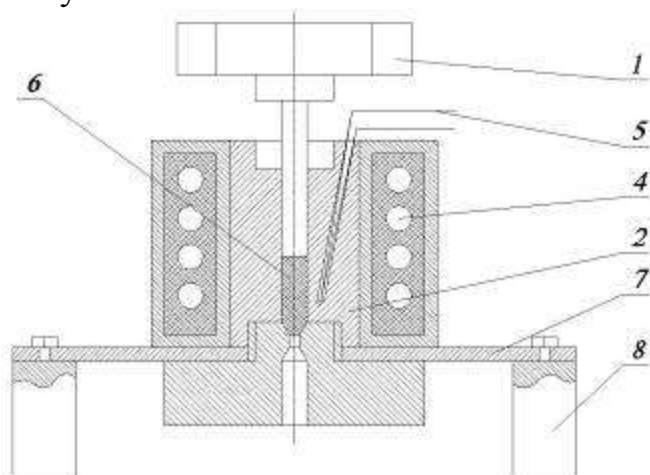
Экспериментальная ячейка для плунжерной твердофазной экструзии термопластов: 1—пуансон, 2— матрица, 3 – фильера, 4 – нагреватель, 5 – терморара, 6 – заготовка термопласта, 7—волнопроводящая пластина, 8—ультразвуковые излучатели
